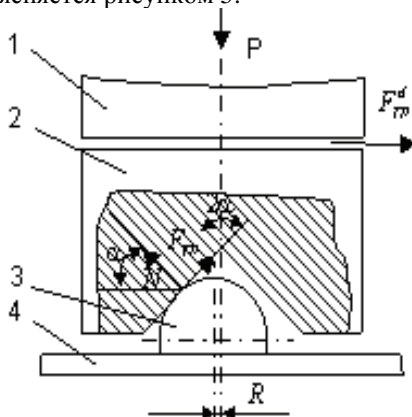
Принципиальная схема устройства: 1 – опора; 2 – матрица; 3 – выступ; 4 – листовая заготовка
